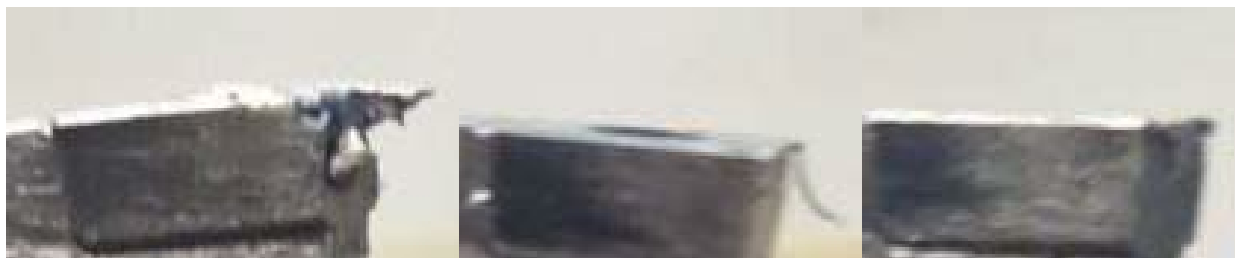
Фотографии налипания металла на режущую кромку твёрдосплавных пластин при резке заготовок с подачей на зуб 0,06мм.
